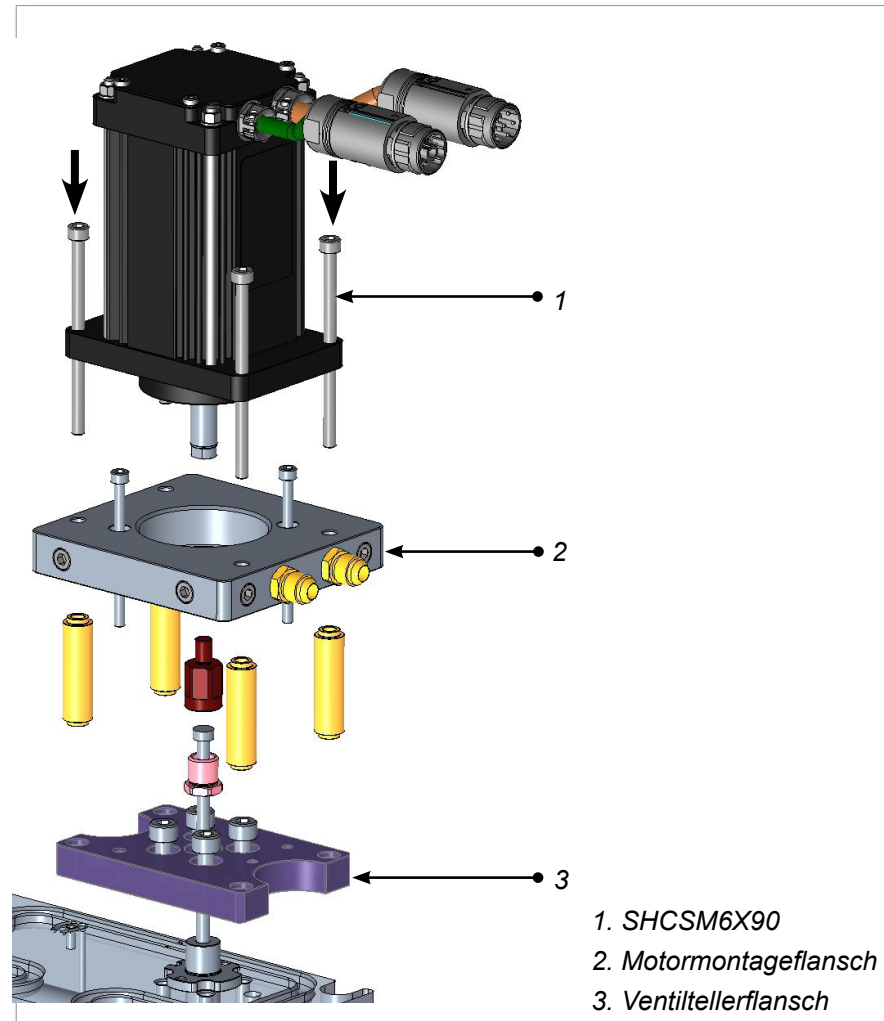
Einsetzen der Schrauben zur Befestigung der Baugruppe
